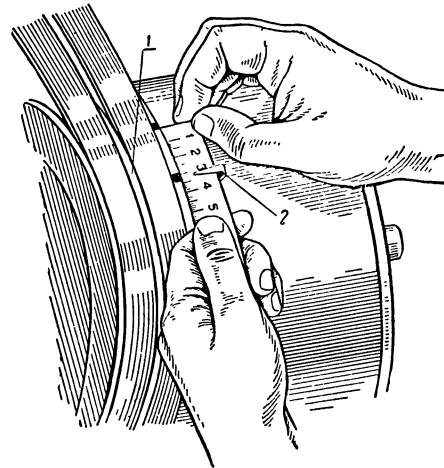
Проверка линейкой расстояния между метками на цилиндрической поверхности буртика шкива.
